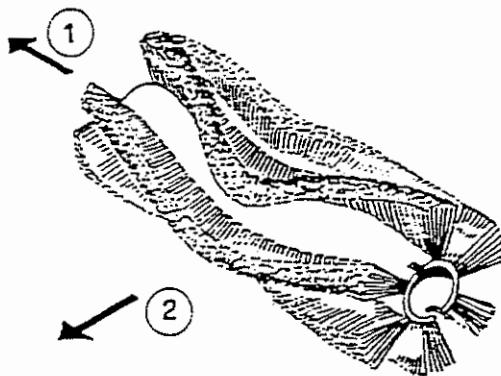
Rappresentazione della spazzola per il senso di montaggio
